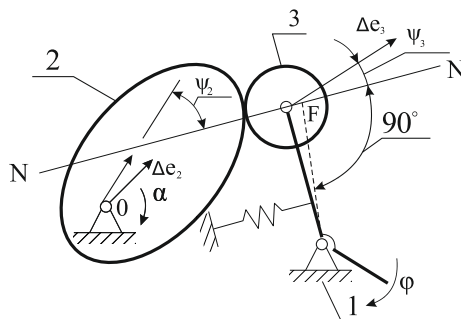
Передача от кулачка к рычагу 1 - корпус; 2 - кулачок; 3 - ролик
